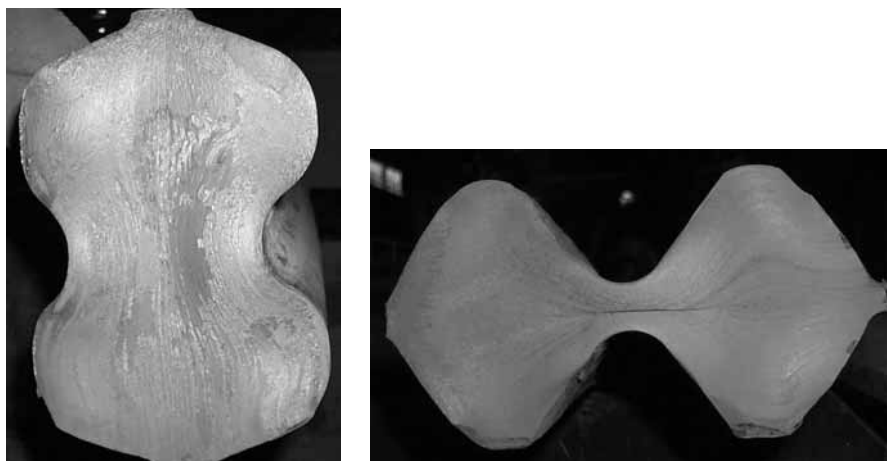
Внешний вид поперечного сечения заготовки при разделении (2-слиттинг)
